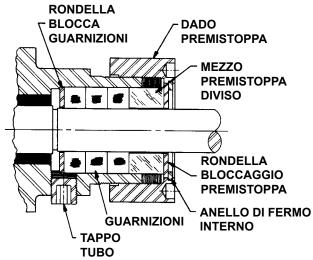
SEZIONE TRASVERSALE AREA GUARNIZIONE TRECCIA (SERIES 724)
